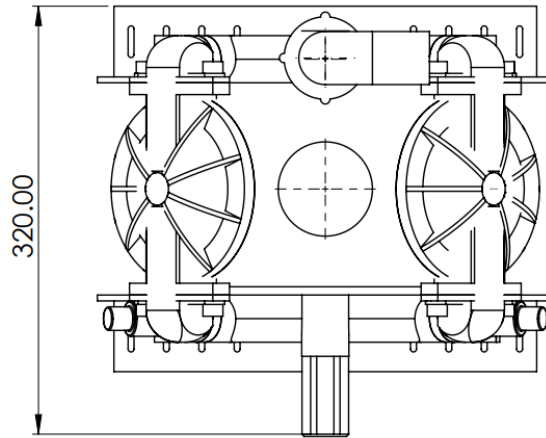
Plano de bomba de membranas IDS 1501 vista de planta (medidas en mm)
